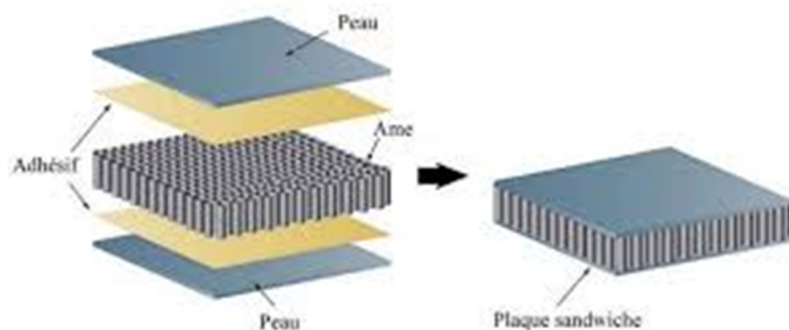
Les peaux Sandwich Typique (Sudharsan et al., 2003).
